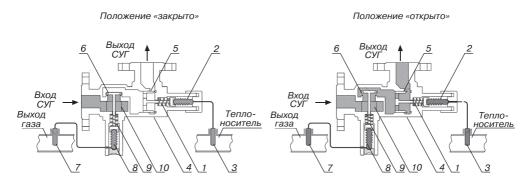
Двухступенчатый термостатический клапан: 1, 9 — пружина; 2, 8 — мембранная коробка; 3 — термодатчик теплоносителя; 4 — корпус; 5, 6 — затвор; 7 — термодатчик СУГ; 10 — фильтр
